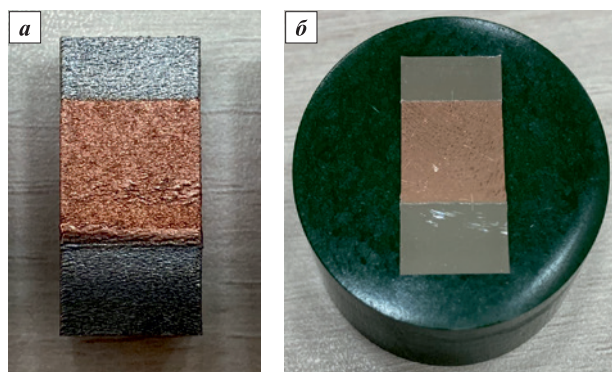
Изготовленный мультиматериальный образец (а) и подготовленный шлиф образца (б)
